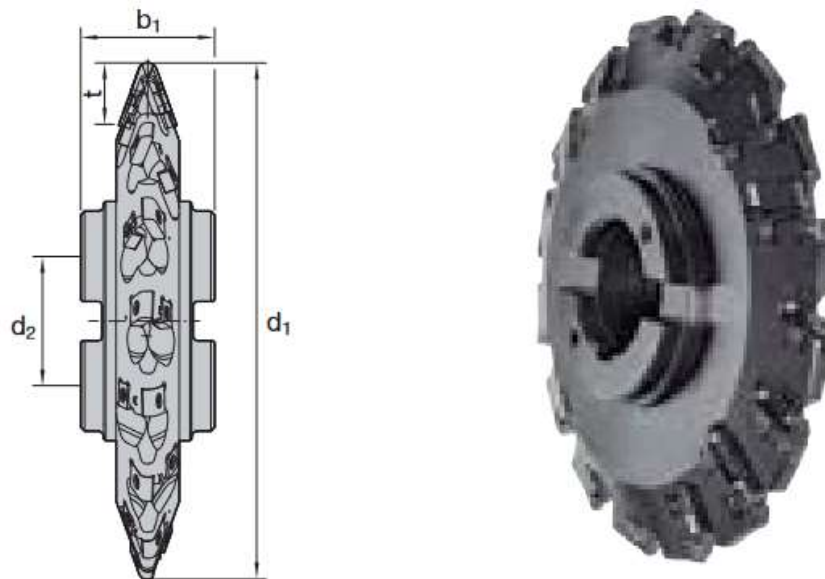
Фрези дискові LMT FETTE для чорнової обробки [18, ст. 96]
